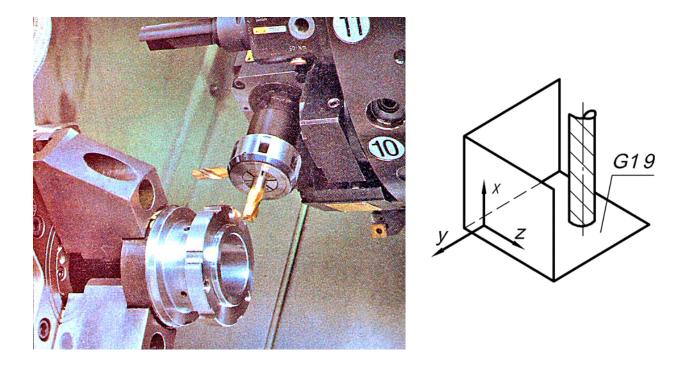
Фрезерный инструмент в плане обработки Y-Z на многофункциональном центре: рабочая зона станка и схема плана фрезерной обработки детали
